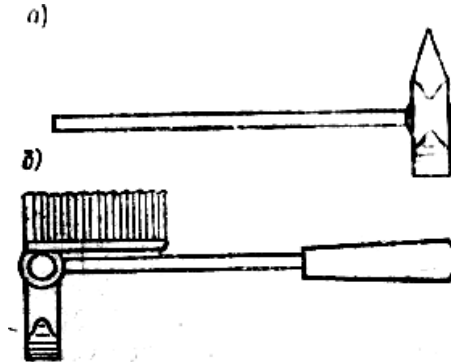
Інструмент зварювальника: а – зубило; б – комбінована щітка з зубилом
